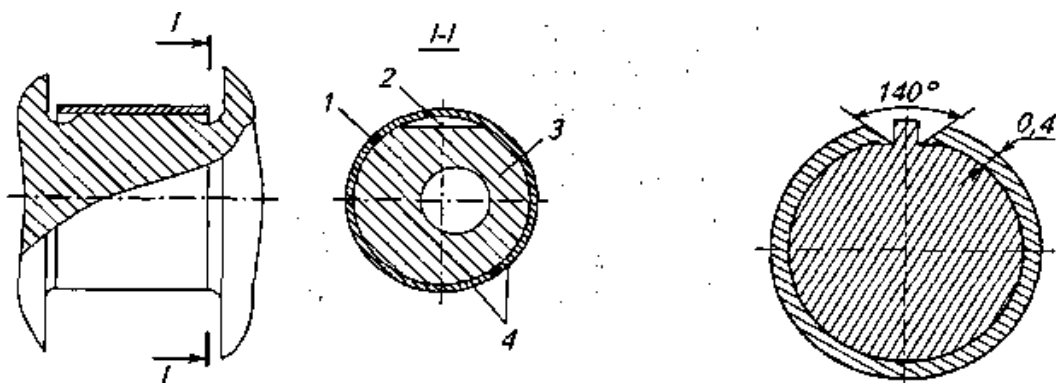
Схема відновлення шийок колінчастого вала двигуна ЗМЗ-53 приваркою сталевих півкілець
